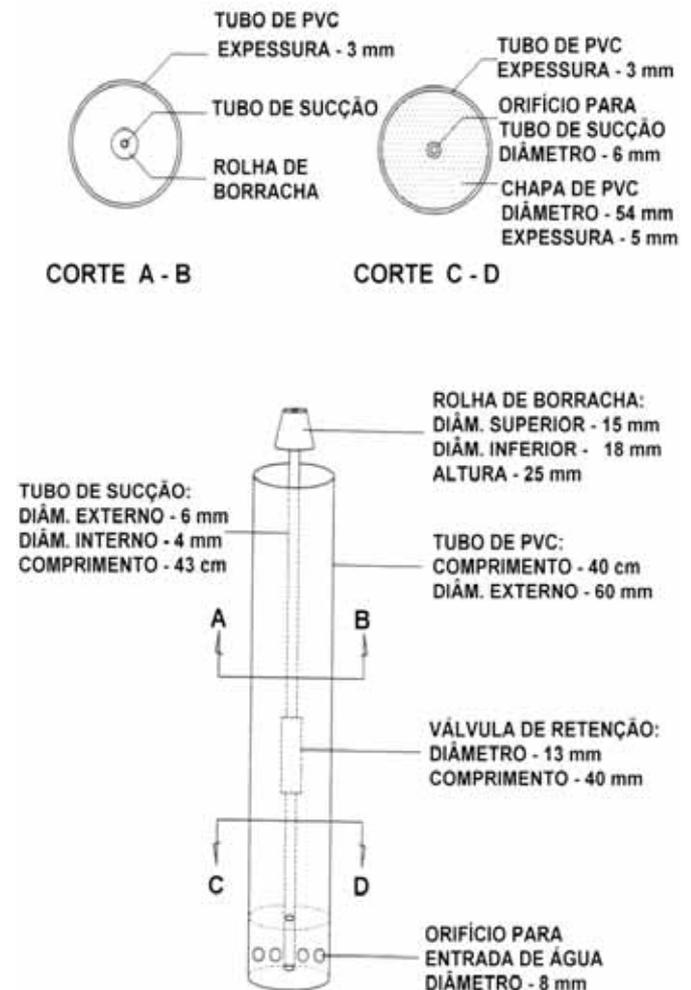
Detalhes construtivos do dispositivo para aumento da resolução de medidas de evaporação do atmômetro modificado SEEL.
